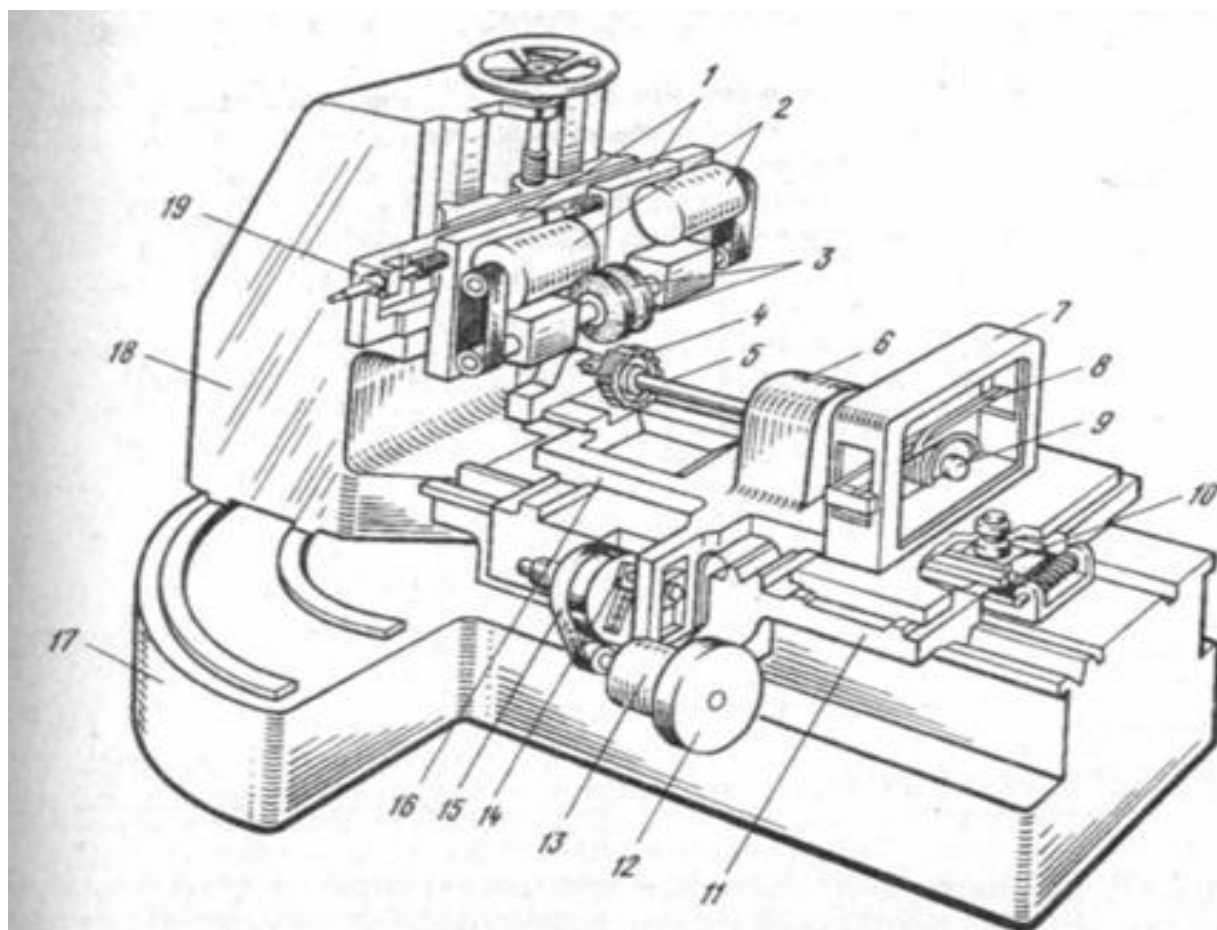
Компоновка зубошлифовального станка с горизонтальной осью, работающего по методу обката с периодическим делением с двумя тарельчатыми кругами: 1 – шлифовальная шпиндельная бабка, 2 – электродвигатели, 3 – шлифовальные круги, 4 – заготовка, 5 – зажимная оправка. 6 – обкаточная головка с делительным механизмом, 7 – стойка с обкаточной лентой, 8 – обкаточные ленты, 9 – обкаточный сектор, 10 – кулисная направ-
